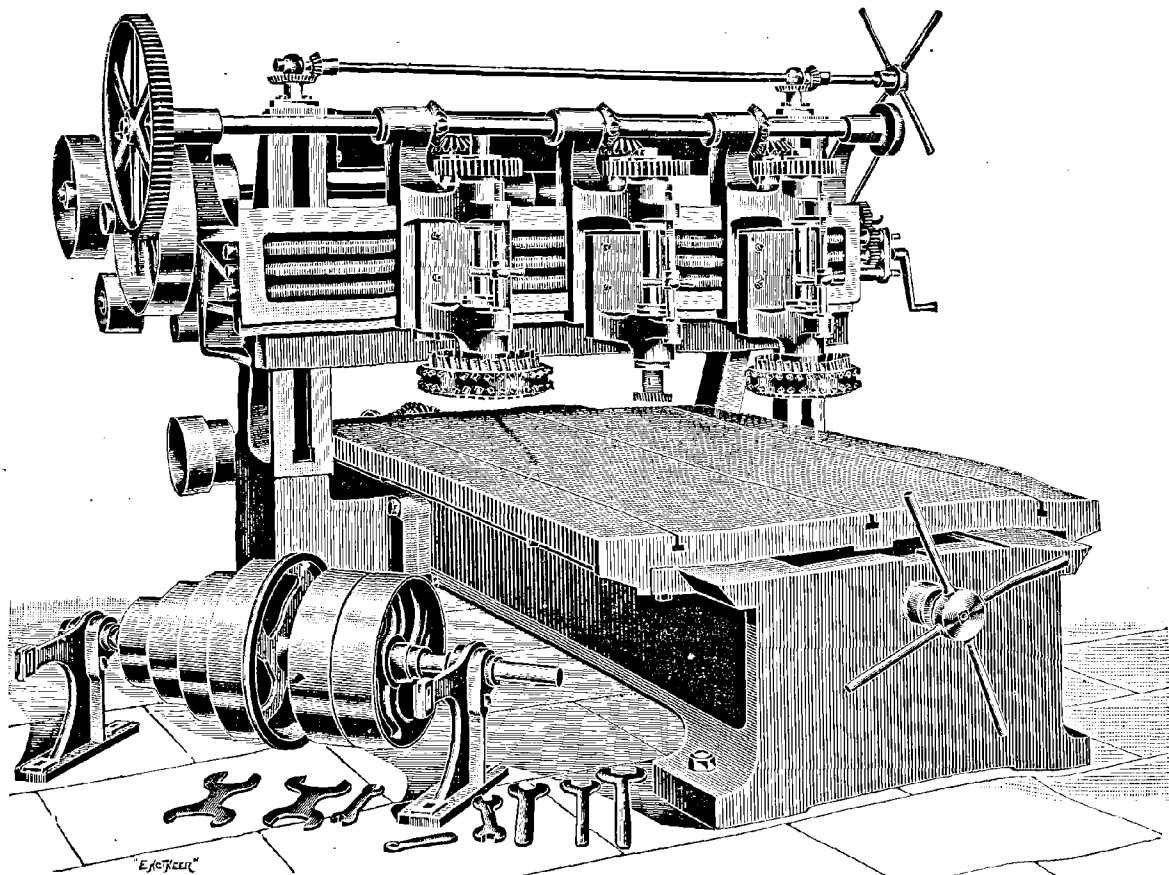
Machine à fraiser verticale à trois outils, type raboteuse de M. Lucas.
